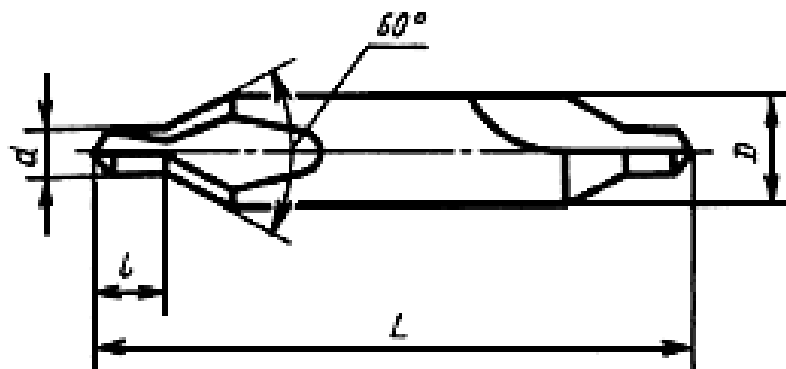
Свердло центрувальне 2317-0003 ГОСТ 14952-75
